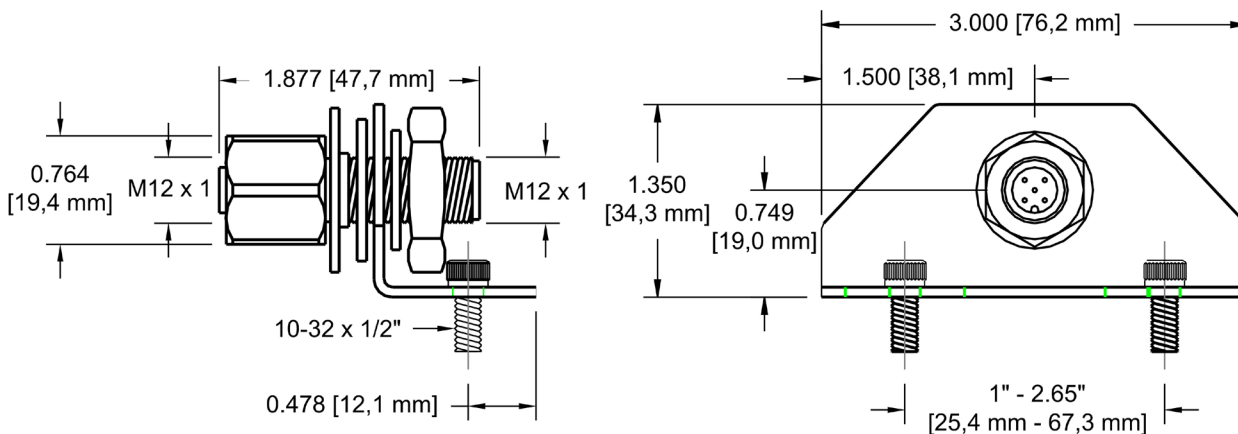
Lynx™ J-LX-B - dessins dimensionnels
